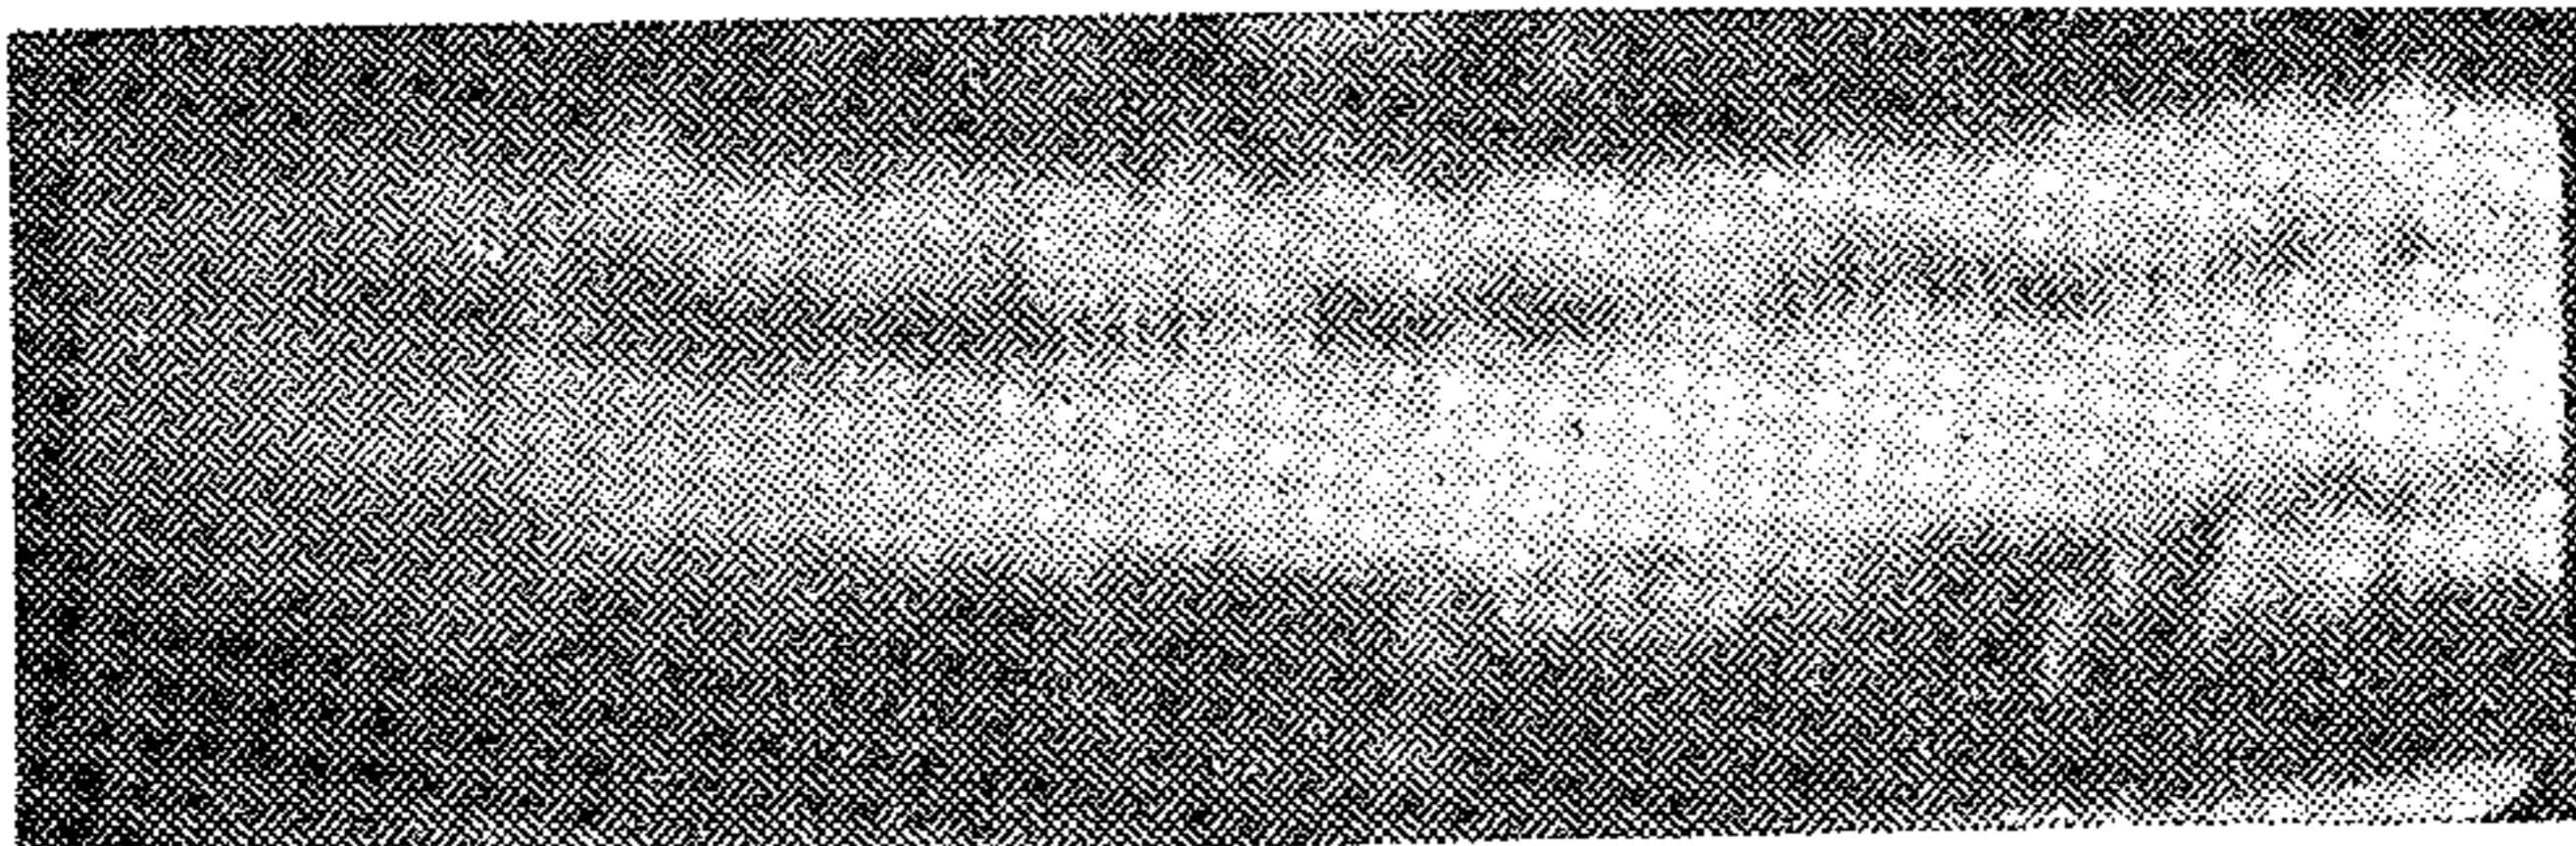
Телевизионное изображение непровара в сварном шве, выполненном ручной электродуговой сваркой с чешуйчатой поверхностью
